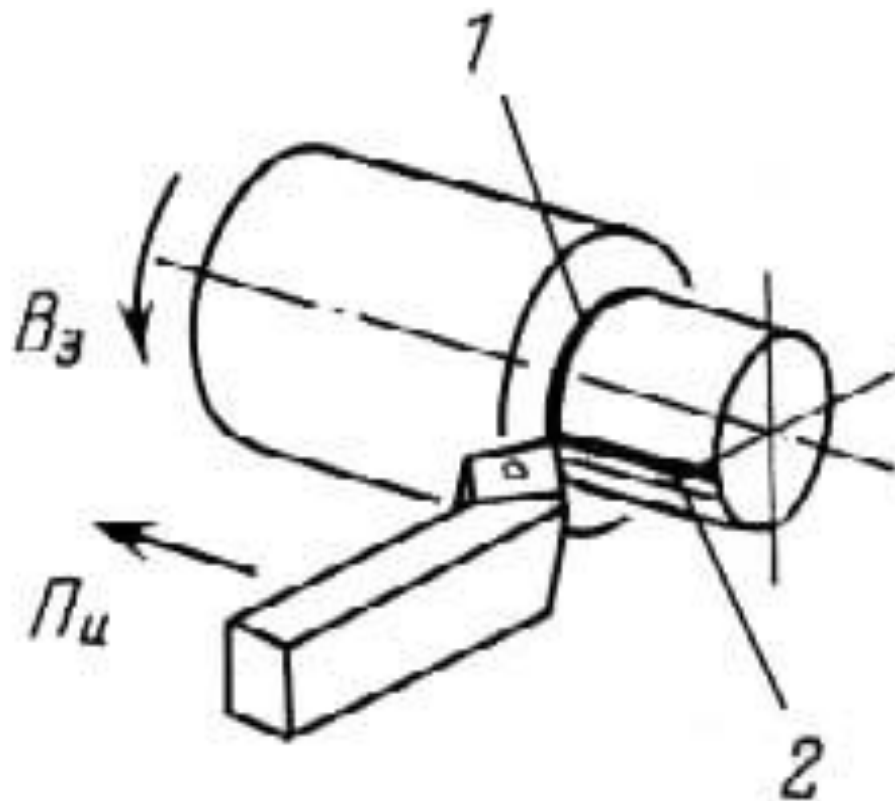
Схема формообразования круговой цилиндрической поверхности: 1 – образующая производящая линия; 2 – направляющая производящая линия; V_3 – вращательное движение заготовки; $\Pi_{ц}$ – прямолинейное поступательное движение инструмента
